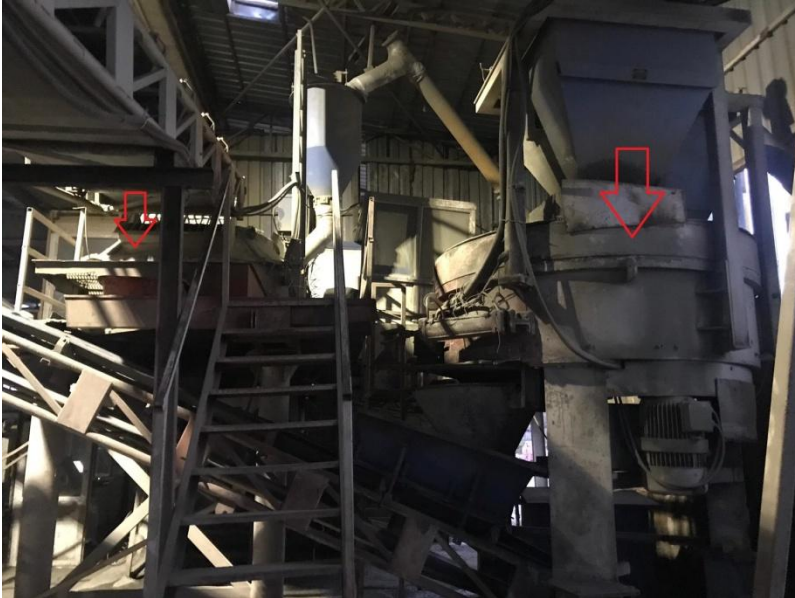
Beton parkelerin üretim şeması (Çevretek, 2013).
